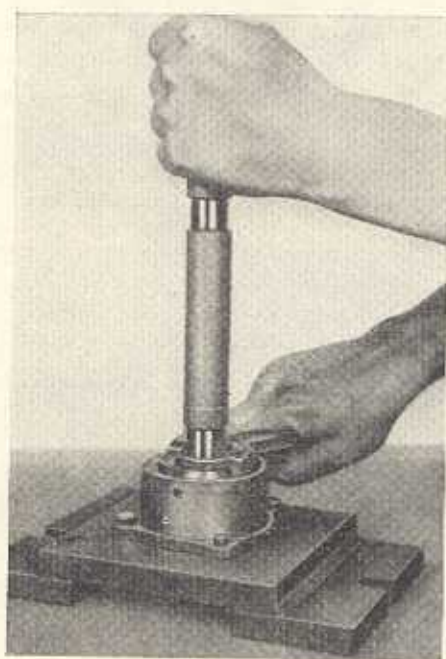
Nutmutter zur Kegelradwelle mit Hakenschlüssel W-86 961/1 herausdrehen
